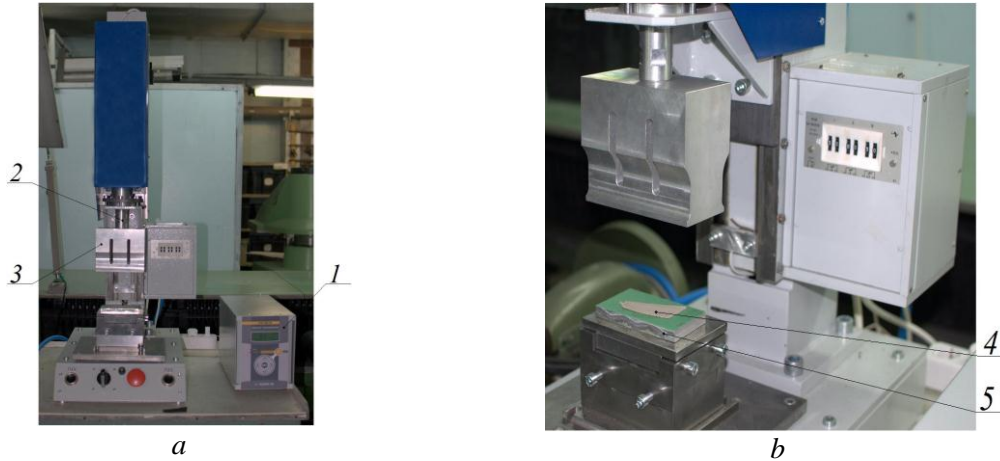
Установка для ультразвуковой опрессовки края обувной резинки:
